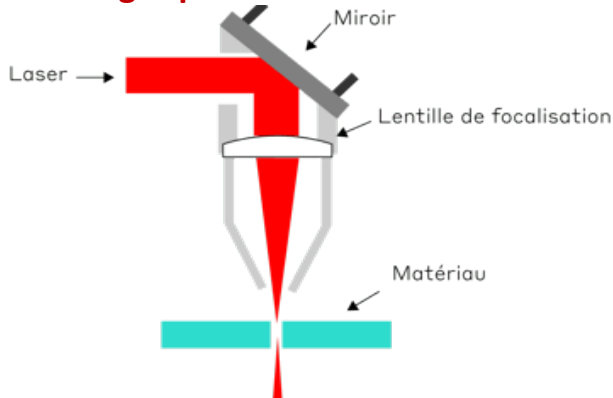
Quelques procédés de soudage avec fusion [7].
